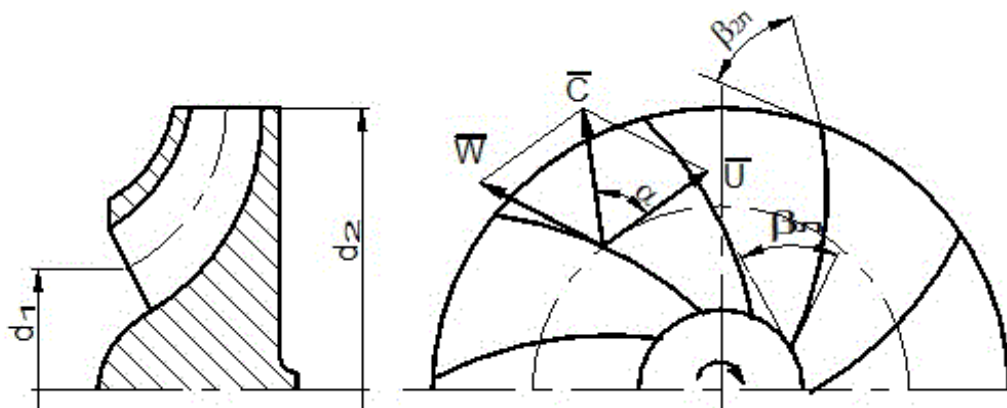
Схема движения потока воздуха в рабочем колесе
